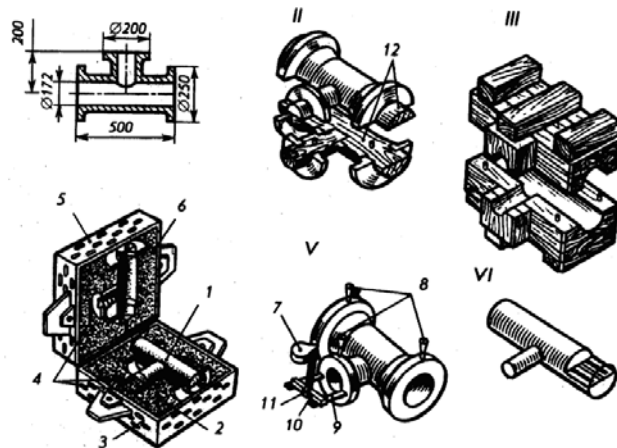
Схема технологічного процесу отримання виливки в піщано-глинясті форми: I – креслення деталі, II - модель, III - стержневий ящик, IV – опоки з сумішшю, стержні, V - виливка, VI – стержень, 1 – стержень, 2 – нижня напівформа, 3 – опока, 4 – канали, 5 – опока, 6 – верхня напівформа, 7 – ливникова чаша, 8 – випори, 9 – подавачі, 10 – шлаковловлювач, 11 – стояк, 12 - стержневі знаки.
